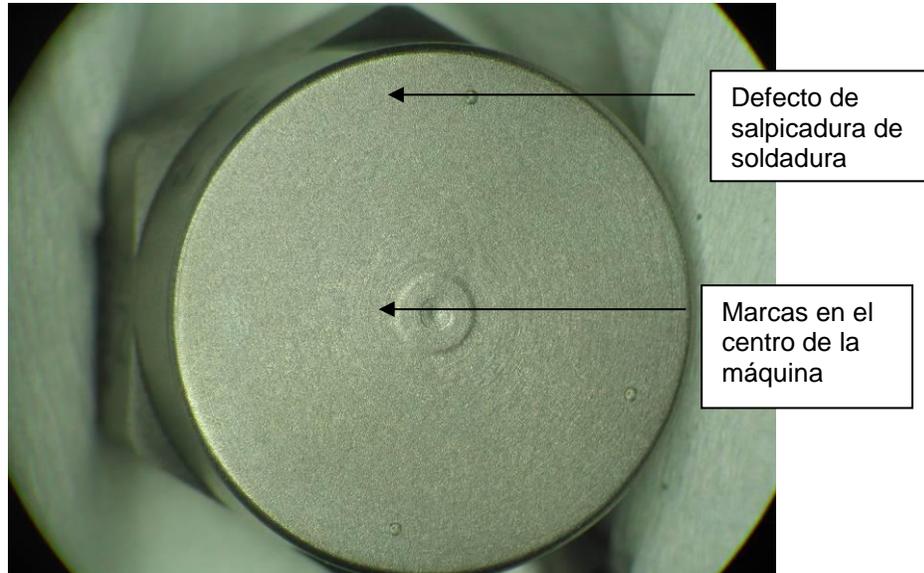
Ejemplo de marca de maquinado y salpicadura de soldadura inaceptables
